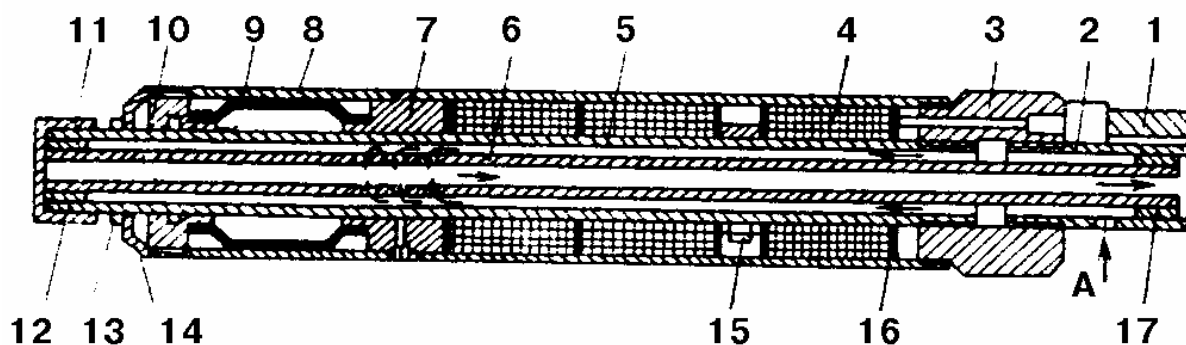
Нагреватель электрический скважинный индукционный НЭСИ50-122М
